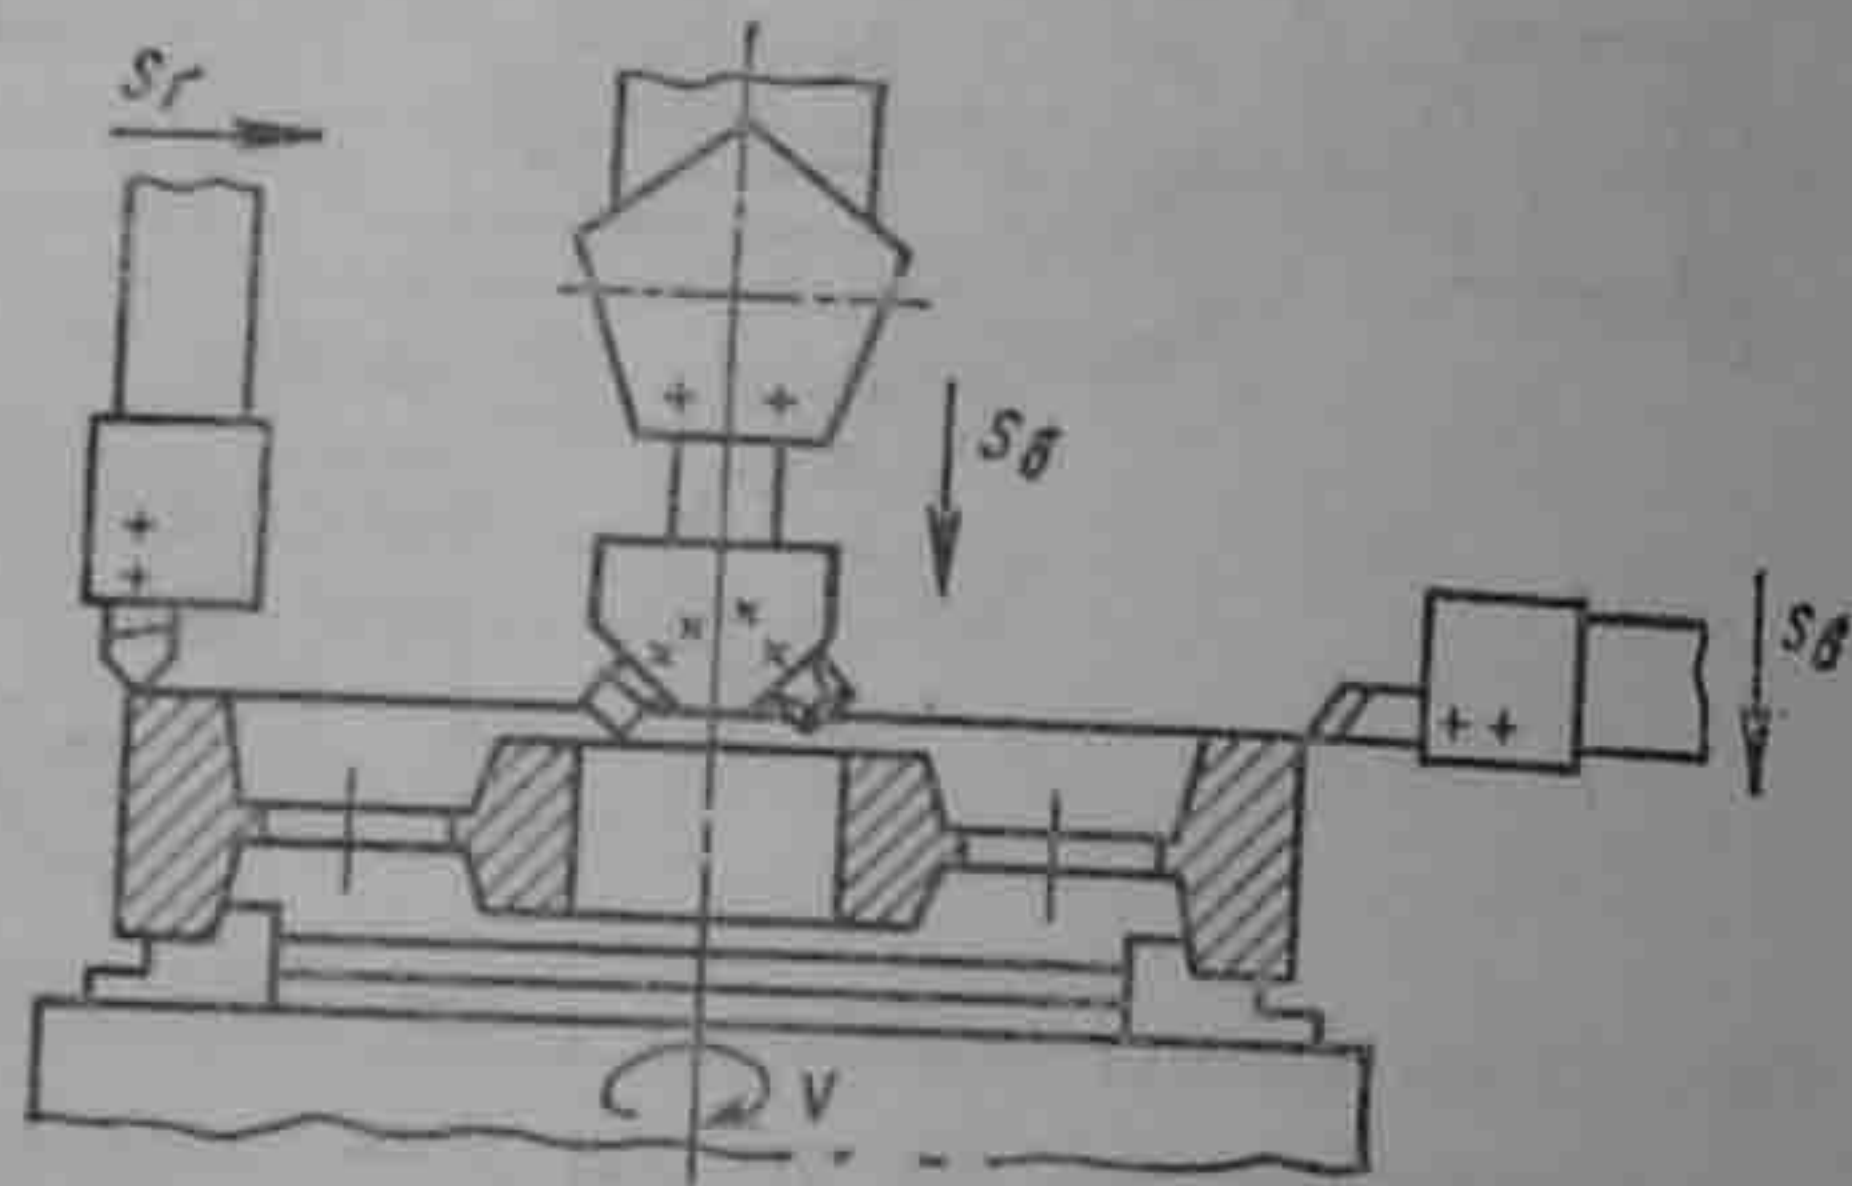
Схема обработки заготовки на токарно-карусельном станке
